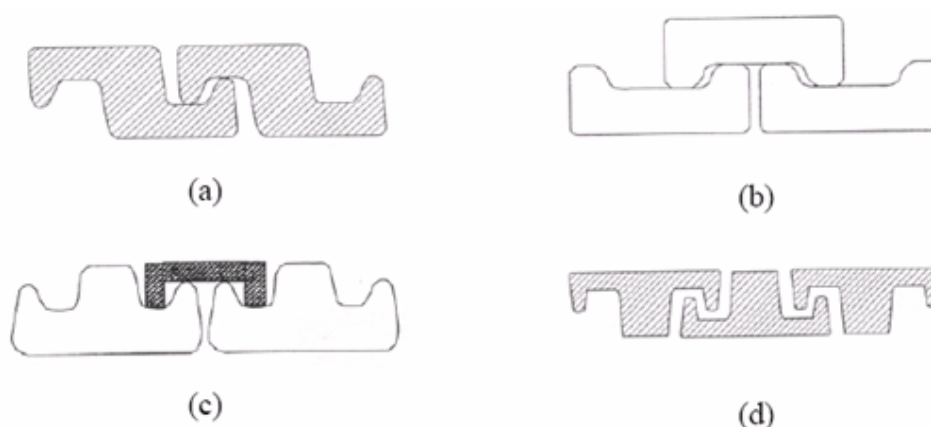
Perfis para a armadura de pressão: (a) perfil Z, (b) perfil C, (c) perfil T (grampo ligando os perfis) e (d) perfil T (API RP 17B, 1998).
